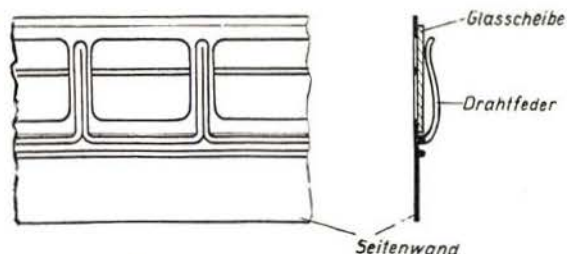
Hinweis für die Befestigung der Dia-Scheiben
